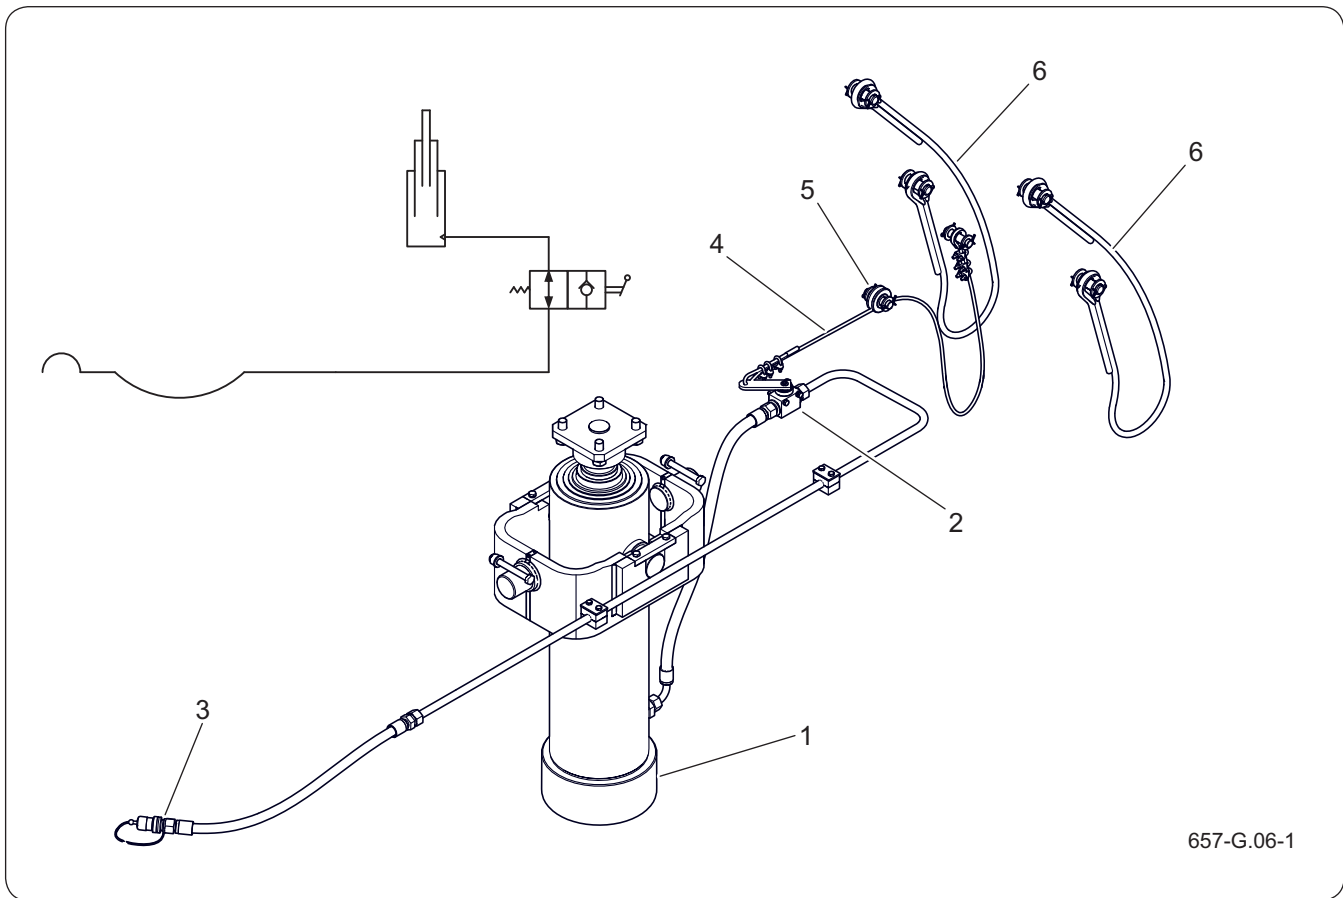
Construction et schéma de l'installation hydraulique du dispositif de basculement
